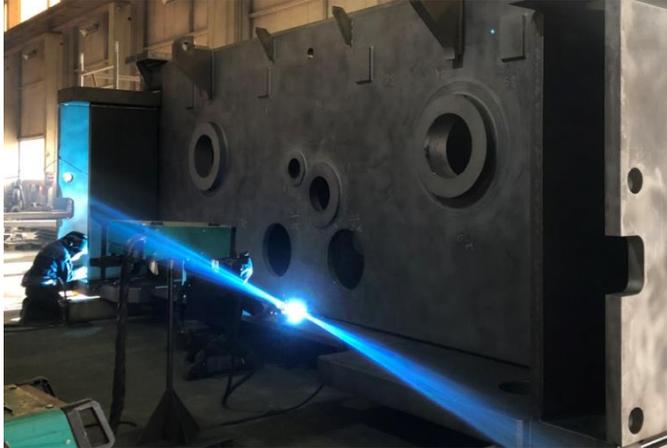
Aus 99 Einzelteilen und Blechdicken von 30 bis 230 Millimetern fertigte Jebens die komplexe Schweißbaugruppe – darunter die vier, jeweils zehn Tonnen schweren Längswände.
